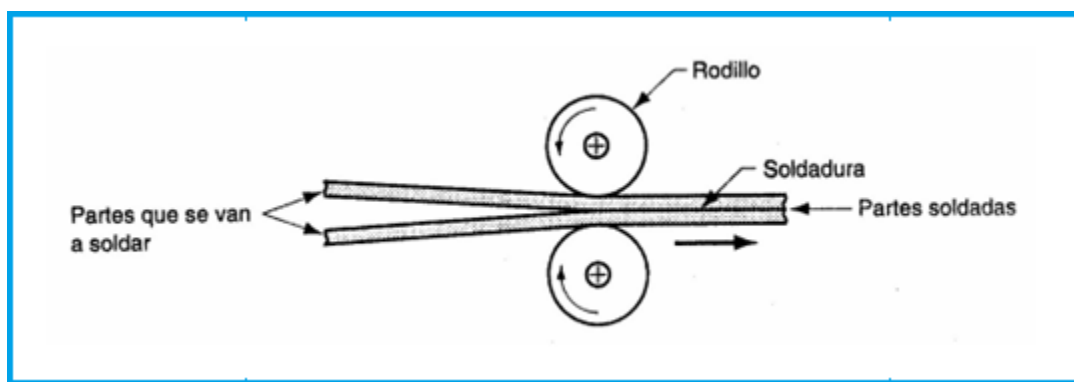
Proceso de soldadura por rodillos.
